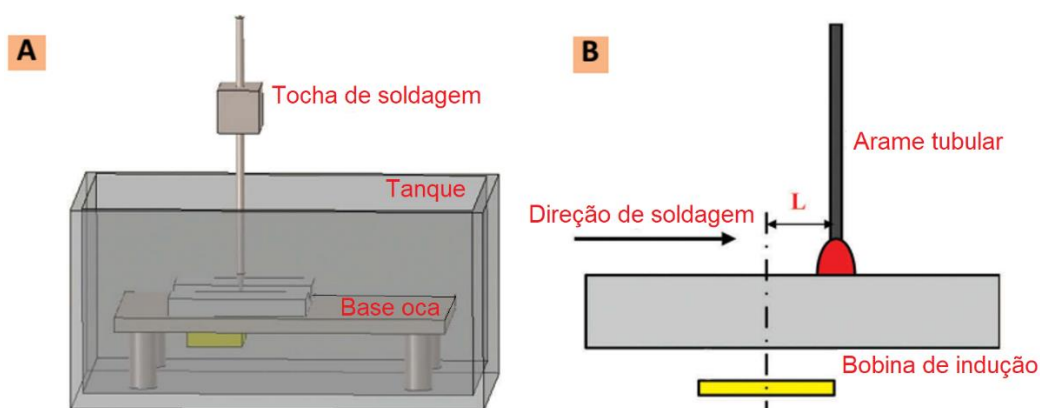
Esquema de montagem dos equipamentos utilizando a bobina de indução.
